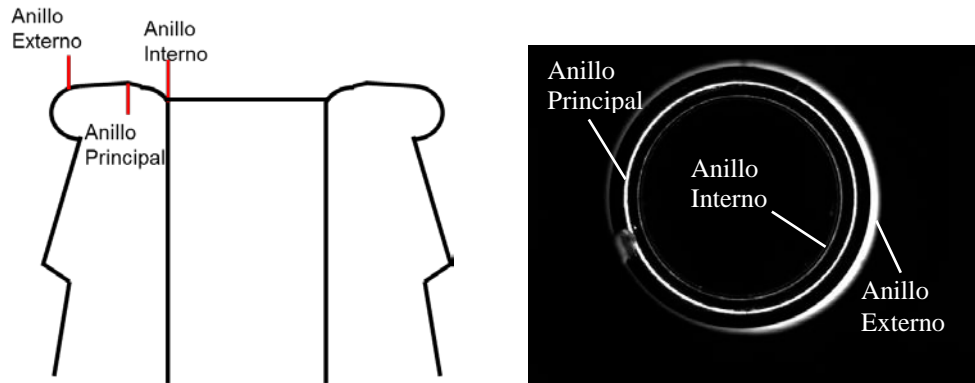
Corte lateral (Izquierda) y vista superior del pico de la botella (Derecha).
